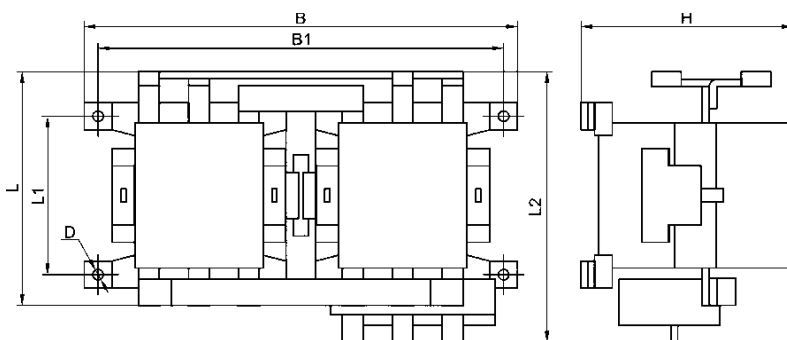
Пускатель реверсивный ПМА-5000, ПМА-6000, IP00
